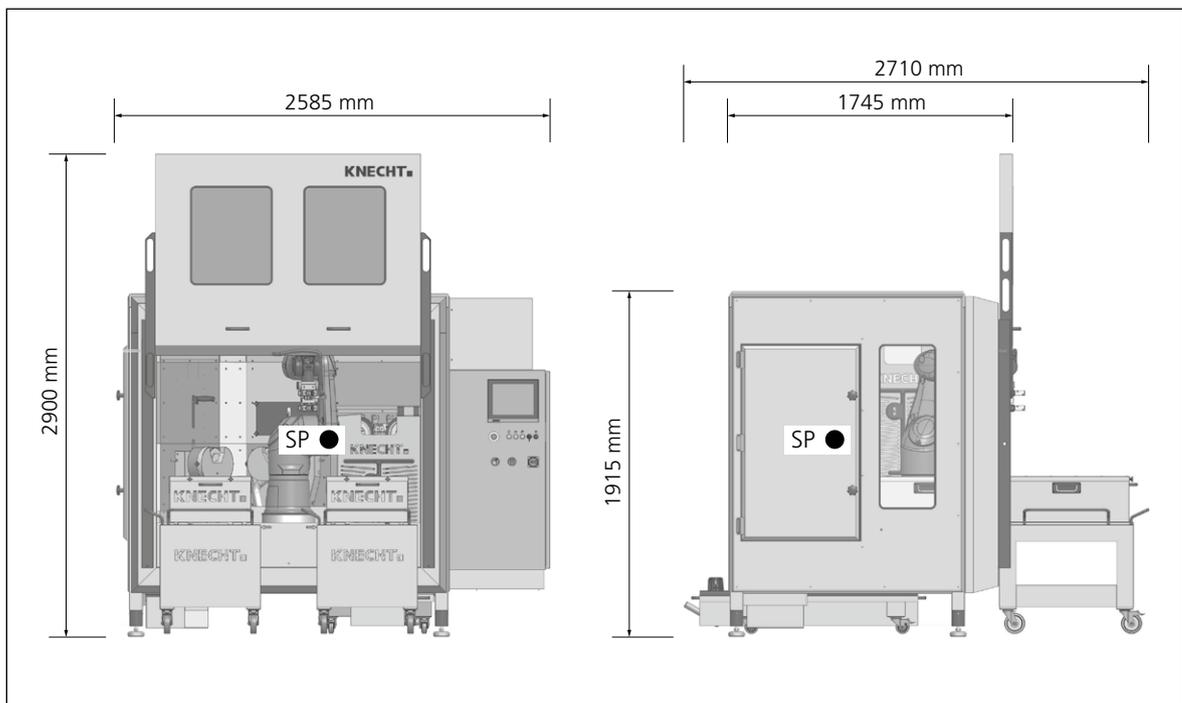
Dimensions en mm et centre de gravité (SP) de la machine
